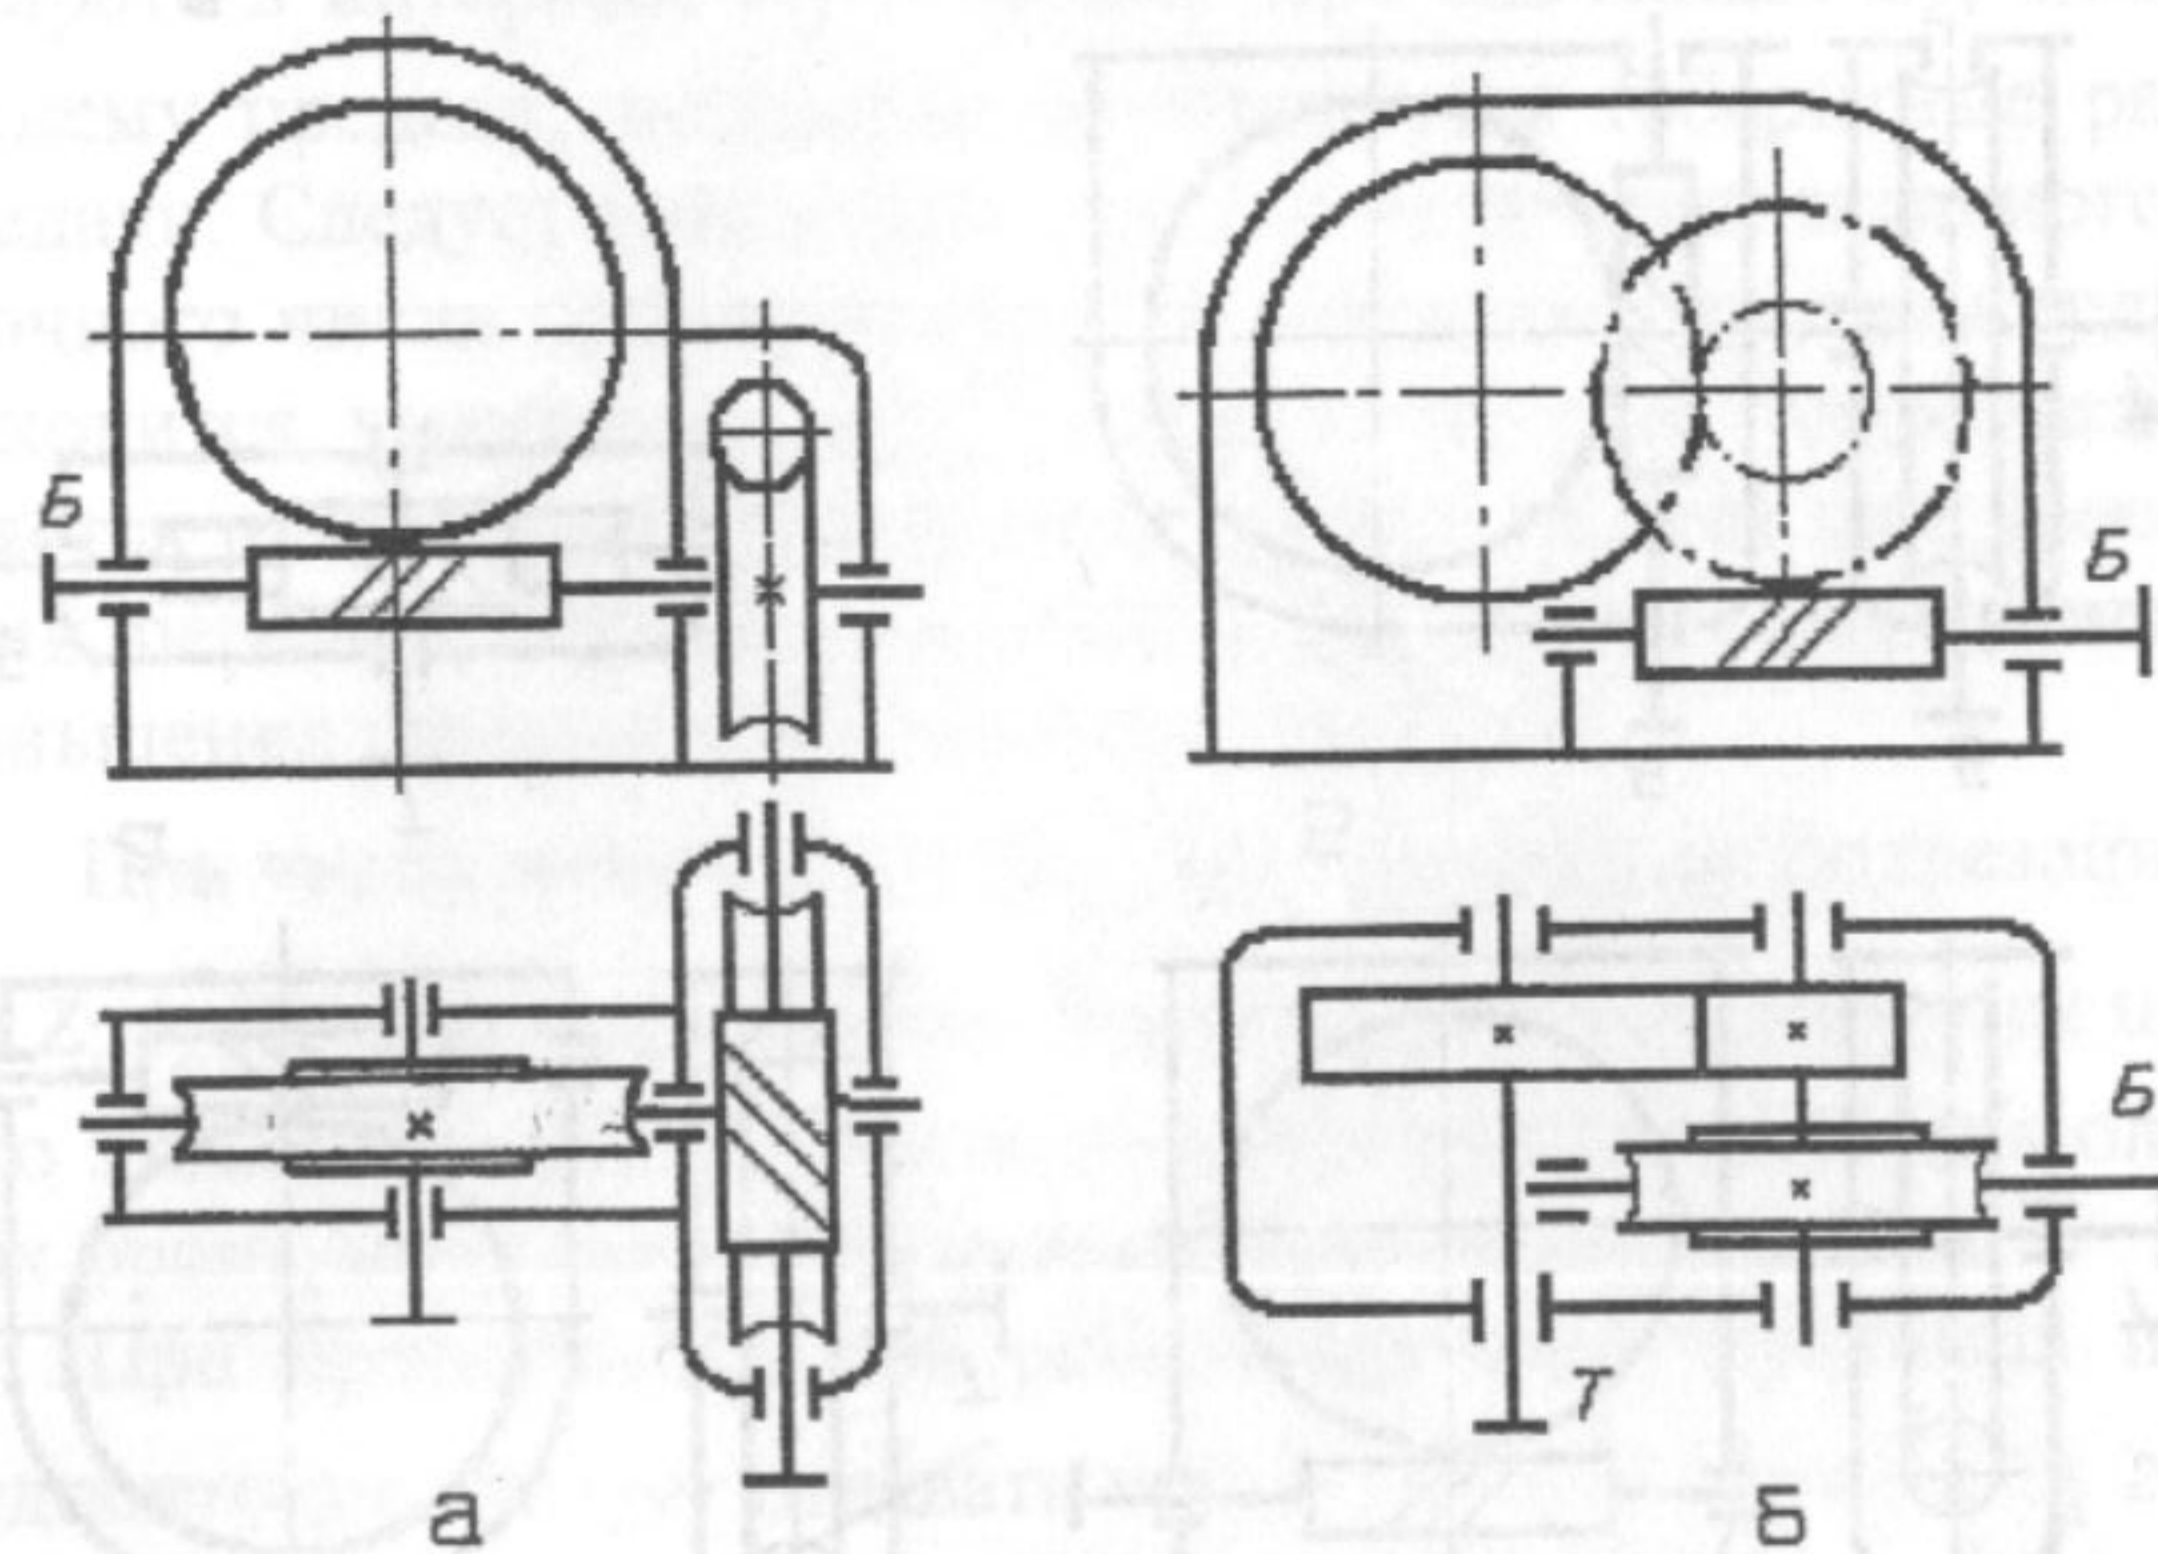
'. Кинематические схемы двухступенчатых червячных редукторов
